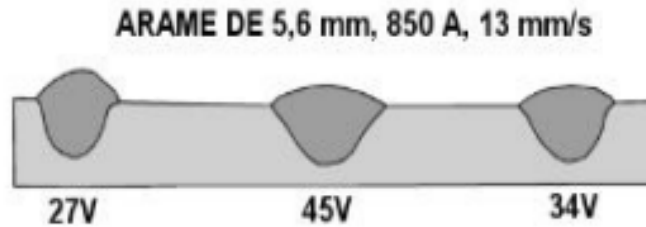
Influência da tensão de soldadura em um processo GMAW com corrente de 850A [33].
